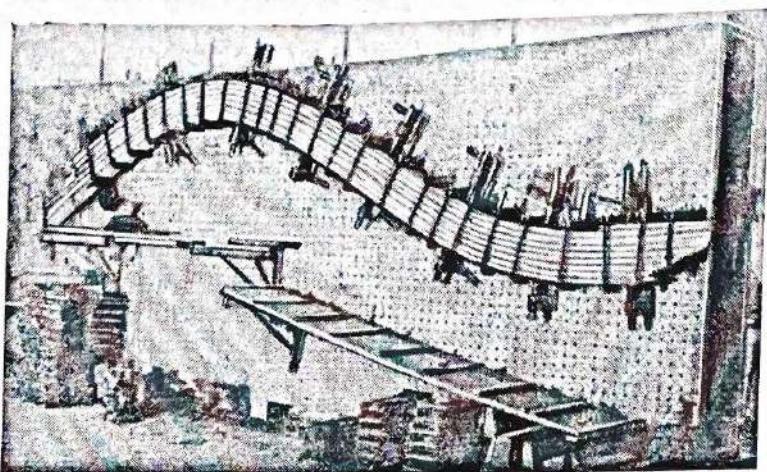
Стенд для запрессовки гнутых kleеных деталей.
